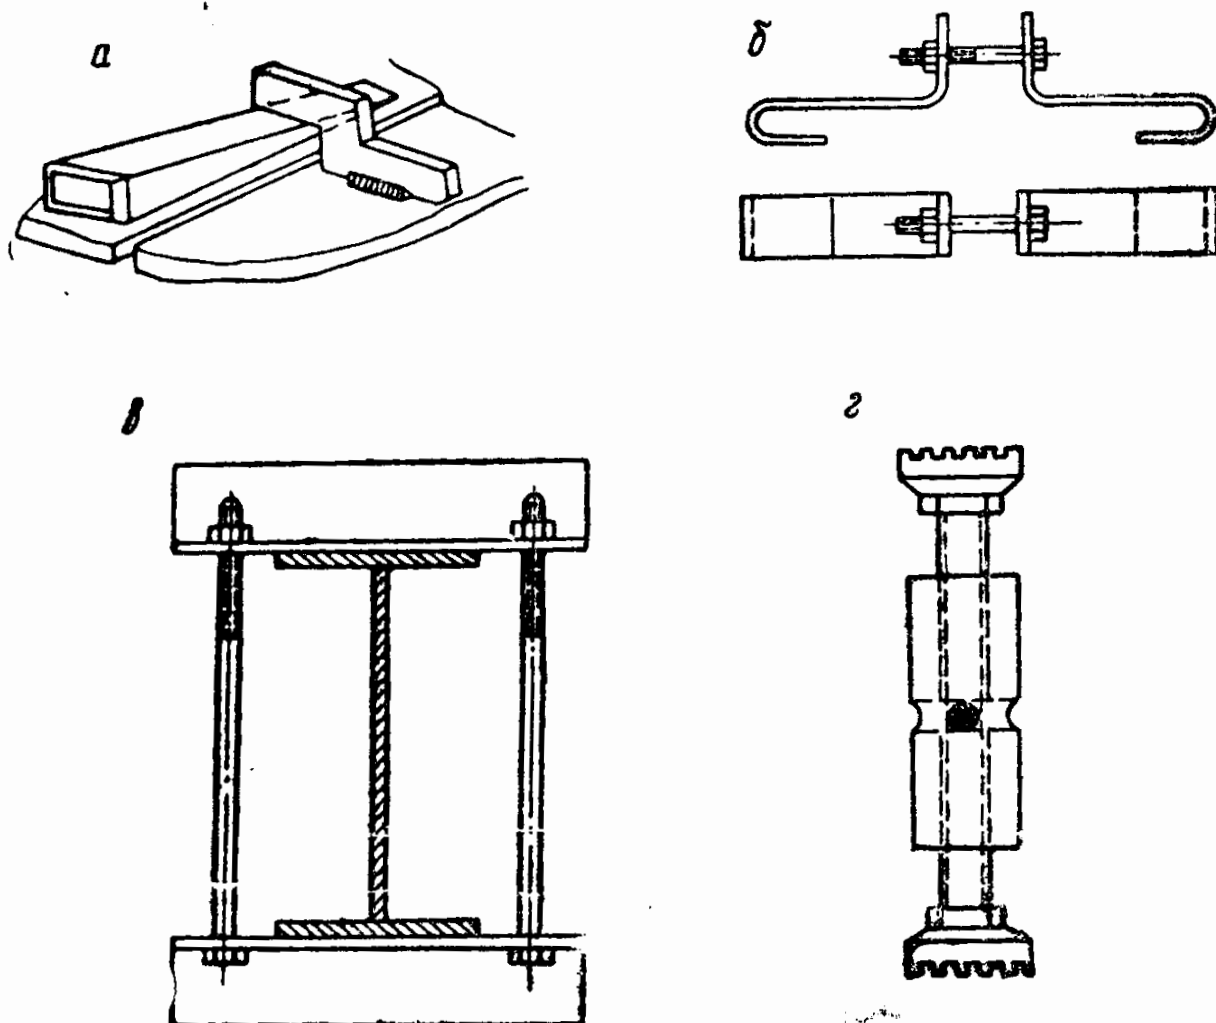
Инвентарные сборочные приспособления: а — скоба с клином; б — стяжное приспособление; в — стяжная рамка; г — стыковая распорка
